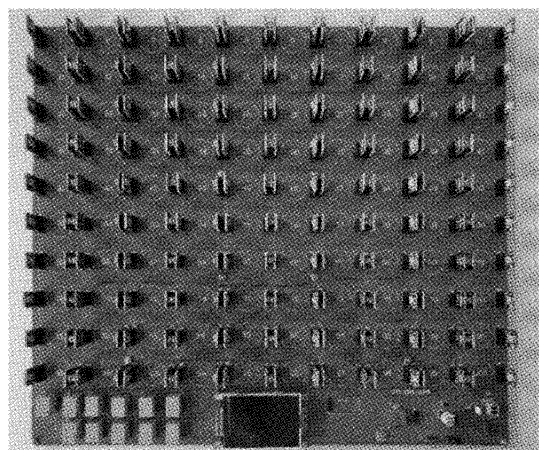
西林瓶灌装药剂监测仪 PCB 板实物图
